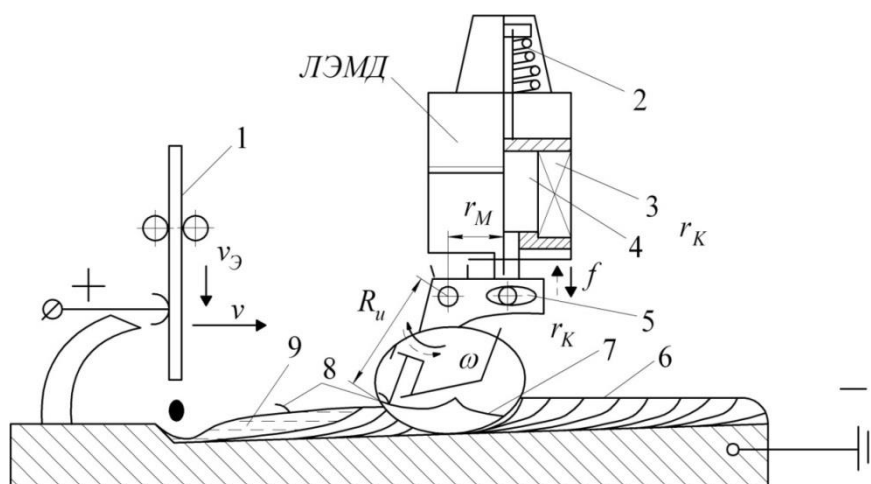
Схема обработки по принципу циклического терморезания с приводом от ЛЭМД: 1 - электрод; 2 - пружина возврата якоря; 3 - соленоид; 4 - якорь; 5 - резец; 6 - обработанная поверхность; 7 - поверхность резания; 8 - стружка; 9 - сварочная ванна;  $v_э$ ,  $v_n$  - скорость подачи электрода и наплавки, соответственно;  $f$ ,  $\omega$  - усилие и частота возвратно-поступательно-качательного движений, соответственно;  $r_k$  - радиус кривизны.
